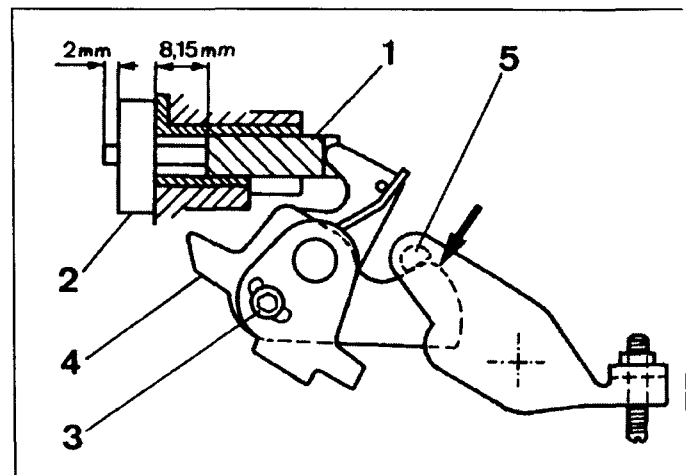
Установка пусковых оборотов - положение кулачка "прогрев"
